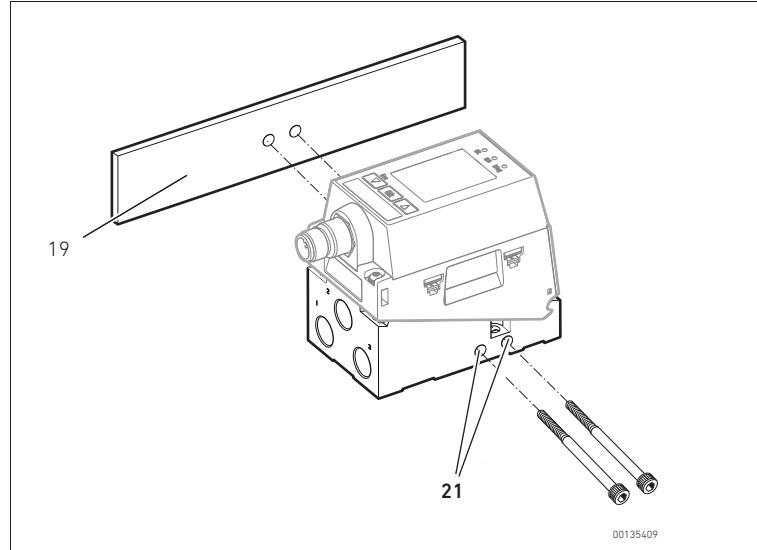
Montaje de la EV03 sobre una placa de montaje con tornillos en los orificios de paso laterales
